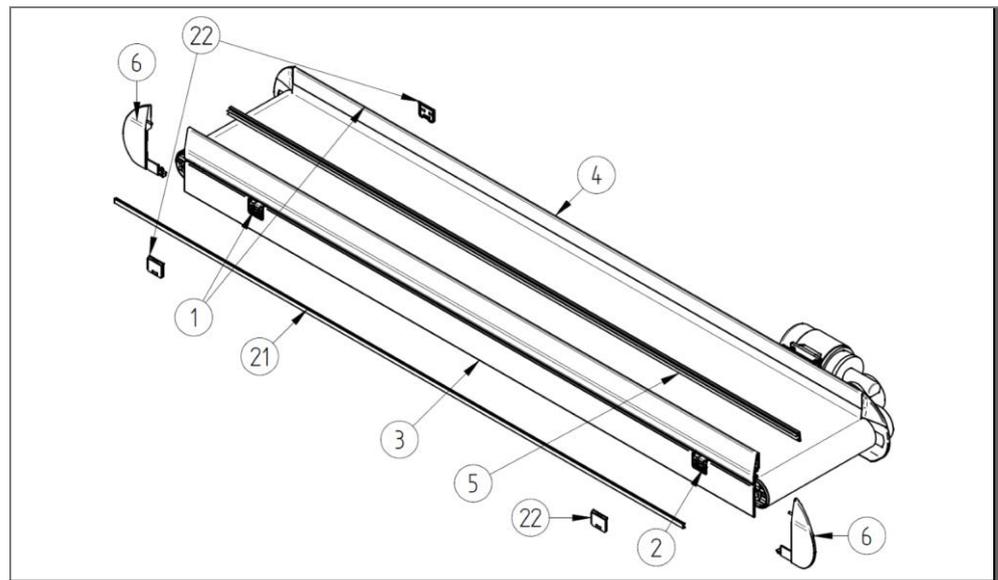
Vue éclatée : Ensemble de bande de convoyage
